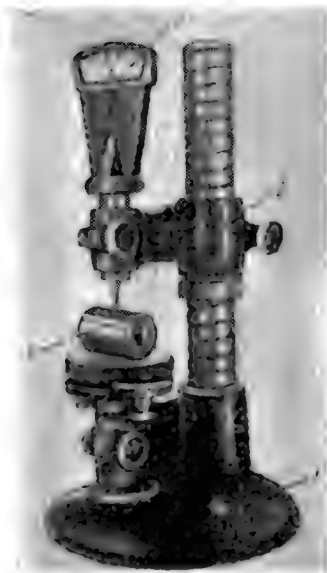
Прибор типа 408М для проверки размеров роликов:
